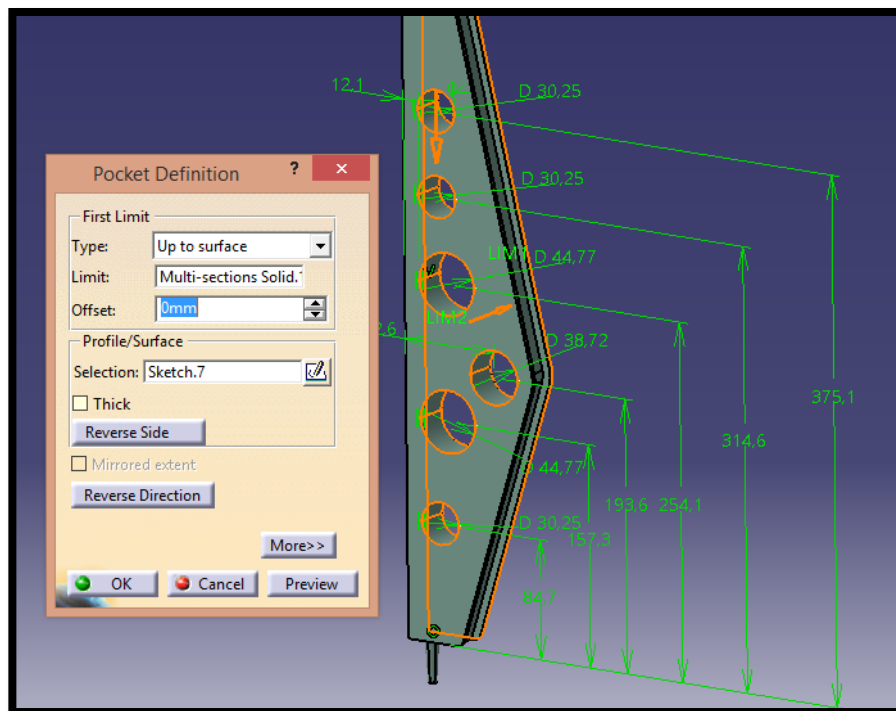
Seat mounting frame 11: Pocket.1 parte principal
